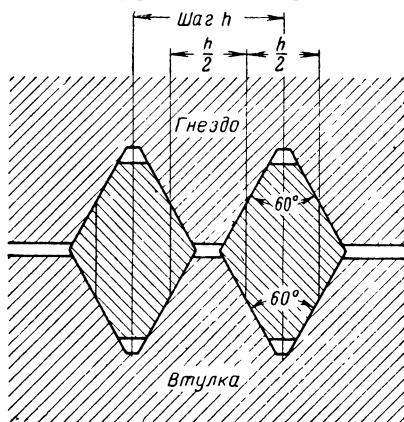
Сечение и размеры одного витка упругой вставки.
